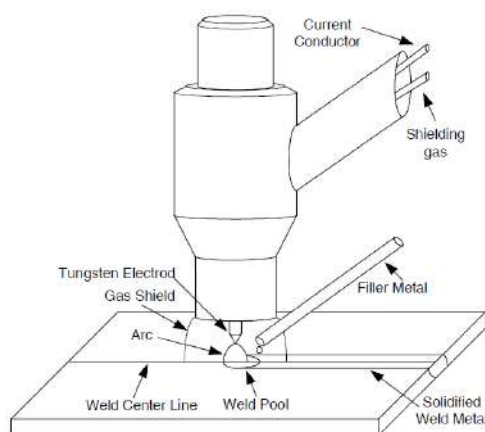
CONFIGURACIÓN DE LA SOLDADURA TIG (ERICSSON, 2003)
